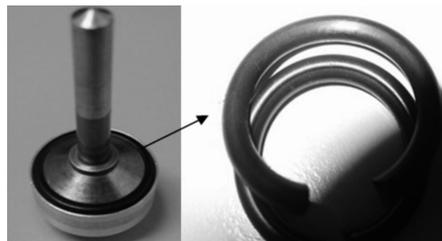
上部活塞新 O-ring 与失去弹性 O-ring 的对比
